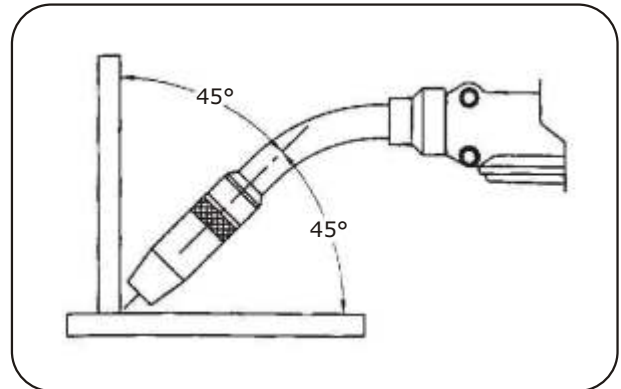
Elektrod Açısının ve Kaynak Tekniğinin Etkileri
